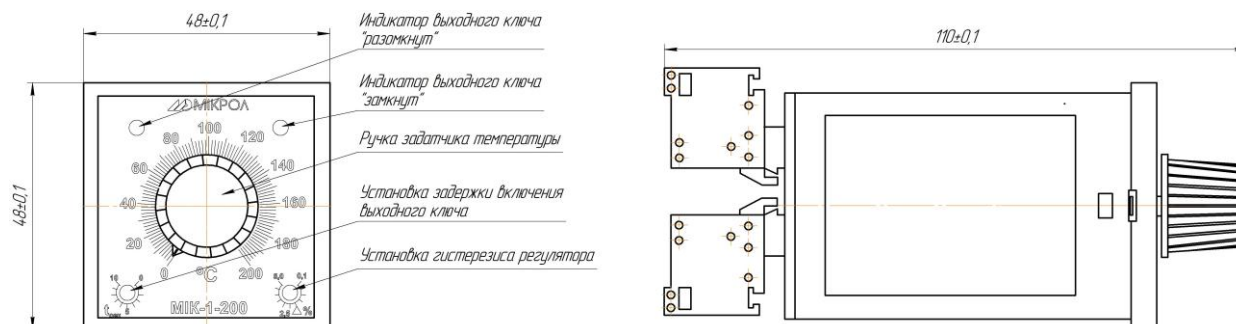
Внешний вид и габаритные размеры МИК-1-200
